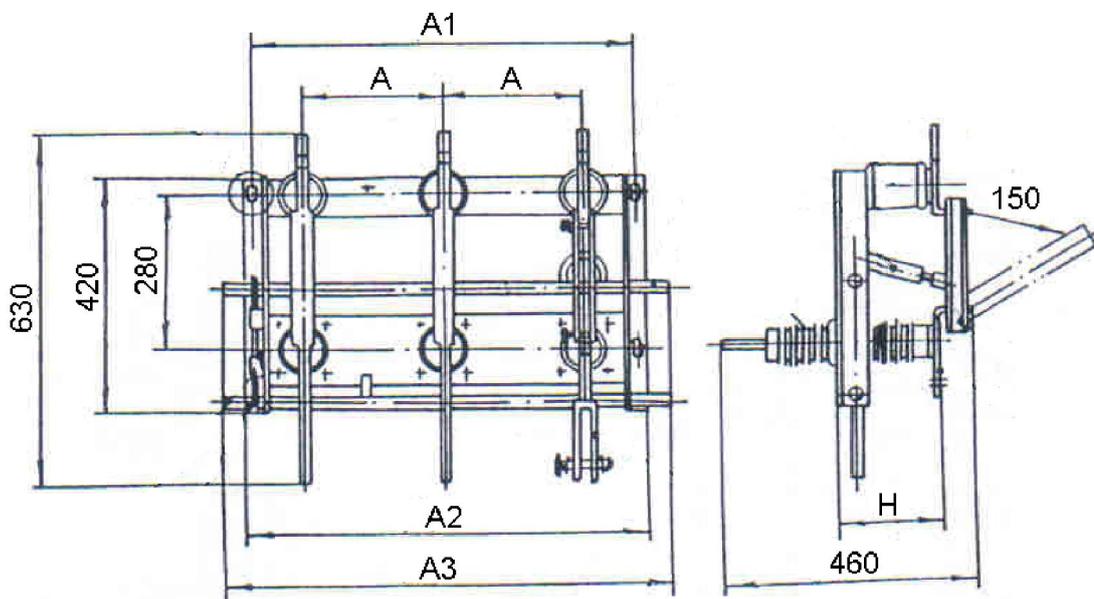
Габаритные размеры разъединителя РВФЗ
